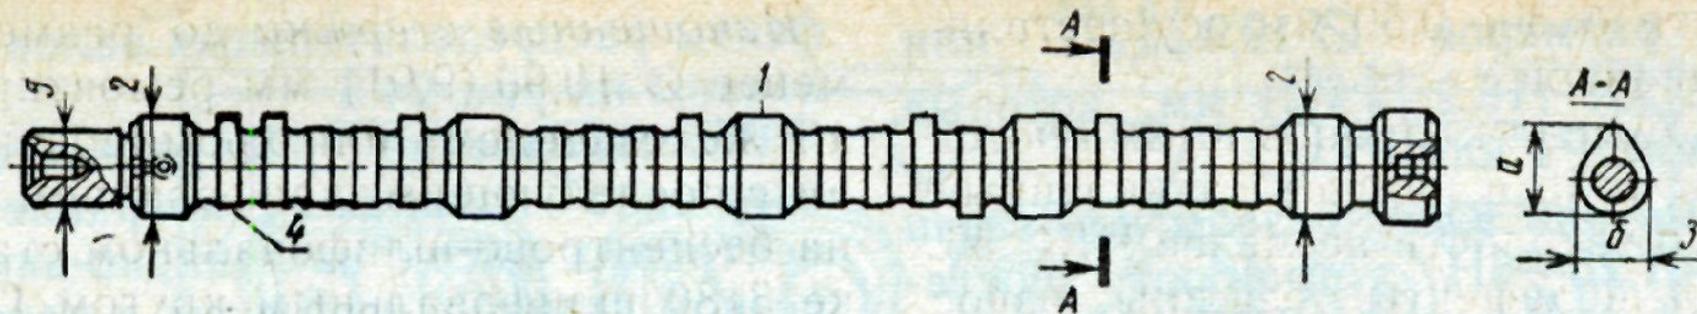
Основные дефекты распределительного вала двигателя ЗИЛ-130:
